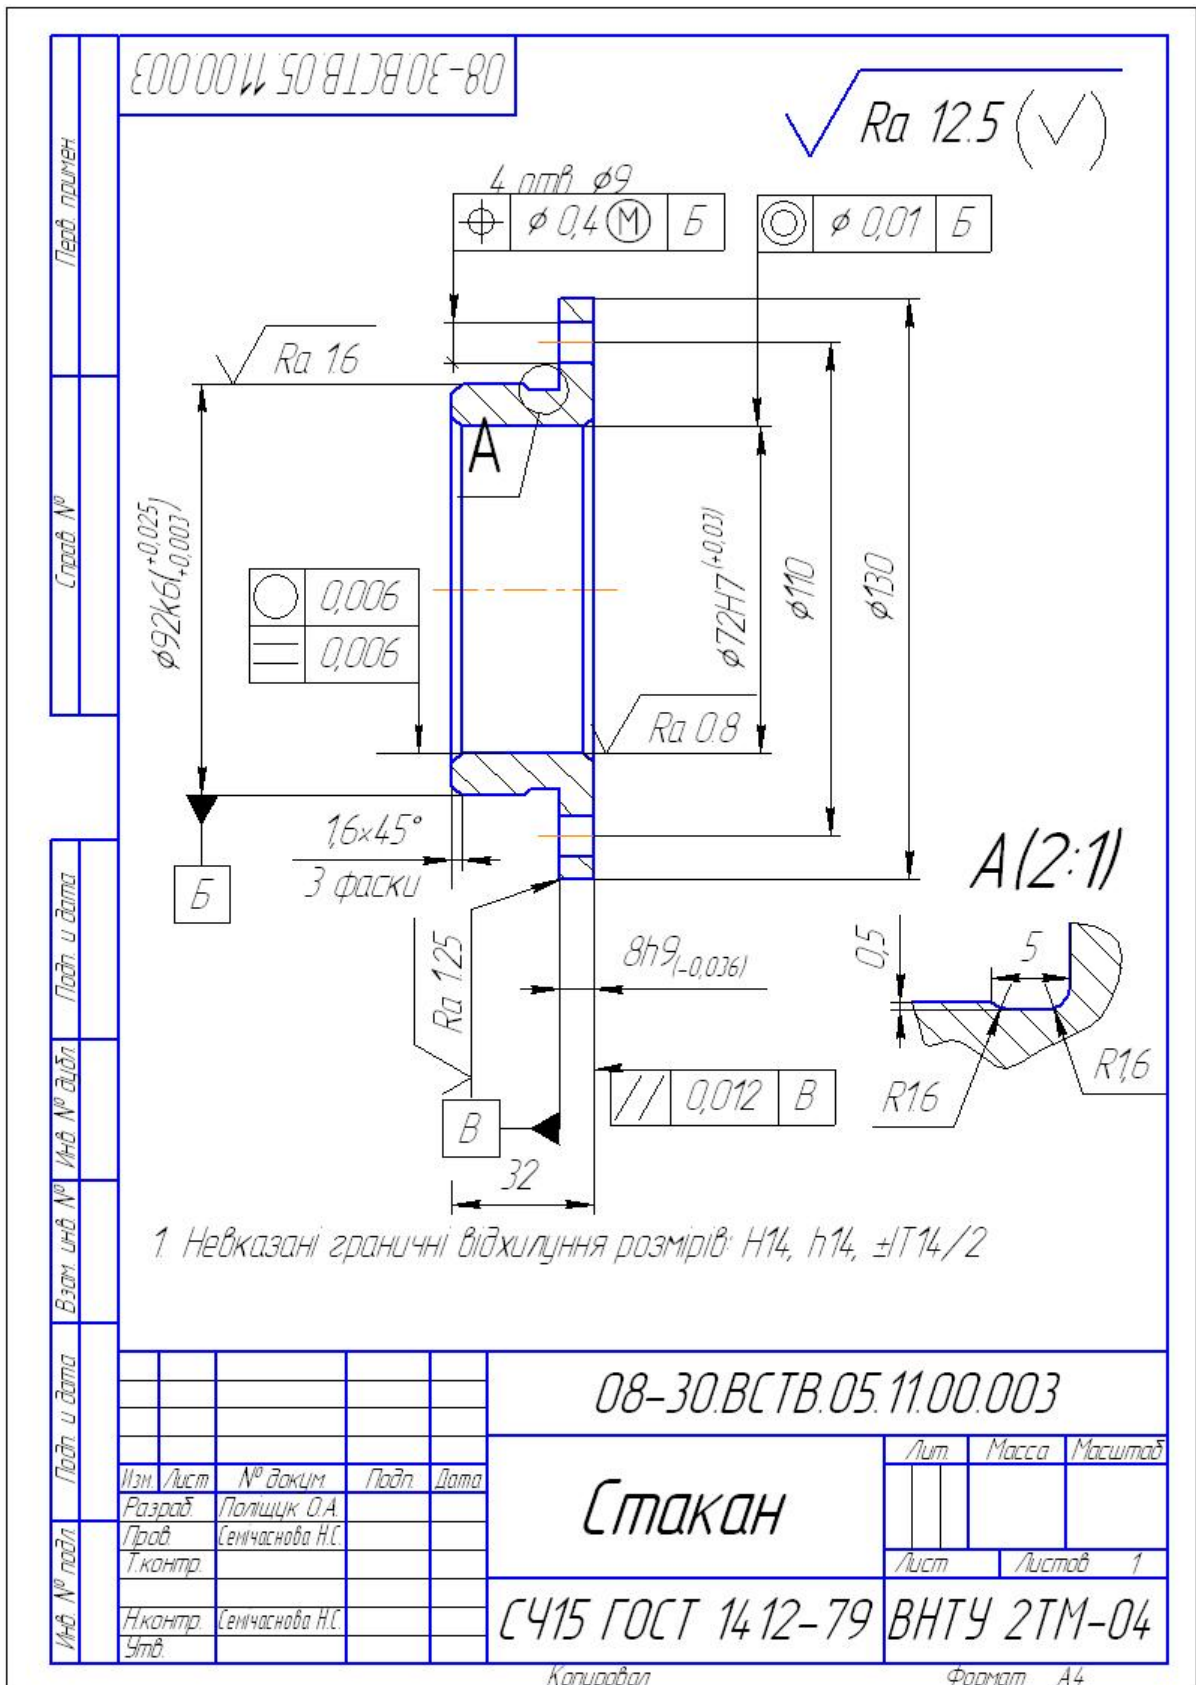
Приклад робочого креслення деталі «Стакан»
